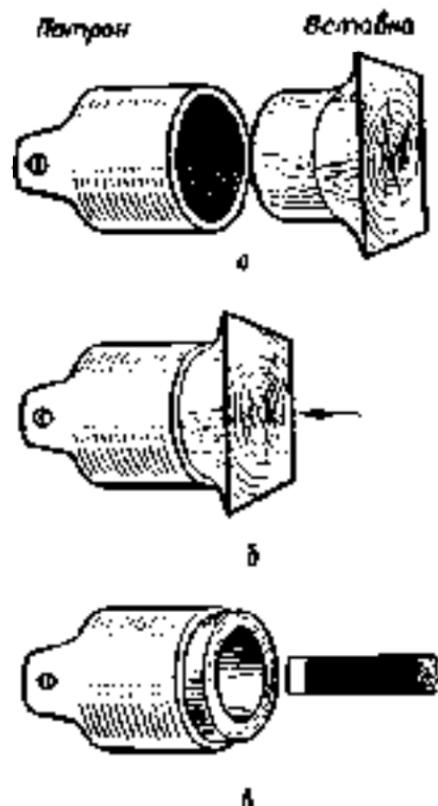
Закрепление в патроне вставки из твердой древесины:
